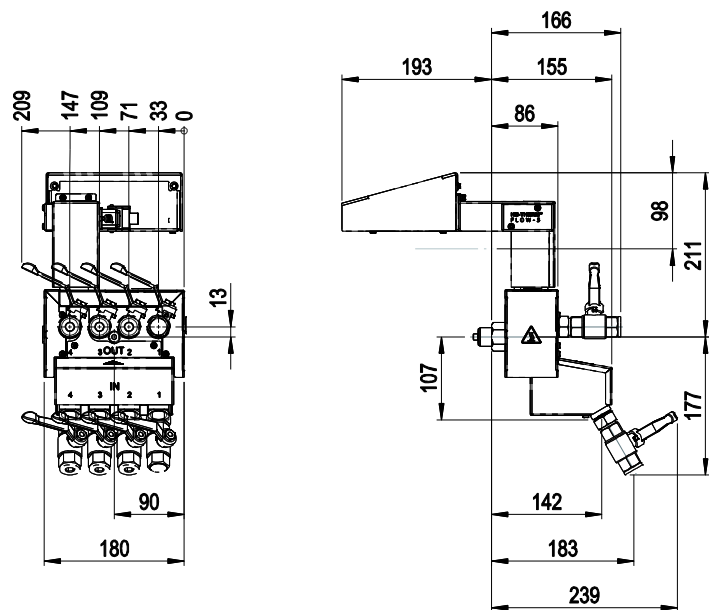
Dimensiuni la modul de construcție montare pe aparat seria 4
